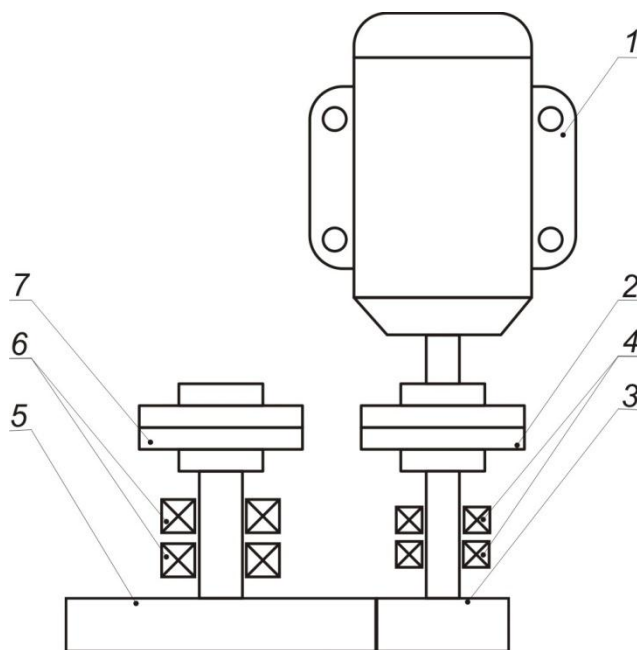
Схема одноступенчатой зубчатой передачи вращательного действия: 1 – асинхронный электродвигатель; 2 – предохранительная муфта электродвигателя; 3 - быстроходный вал-шестерня; 4 – опорные подшипники быстроходного вала; 5 – тихоходный вал с надетым на него зубчатым колесом; 6 – опорные подшипники тихоходного вала; 7 - предохранительная муфта редуктора
